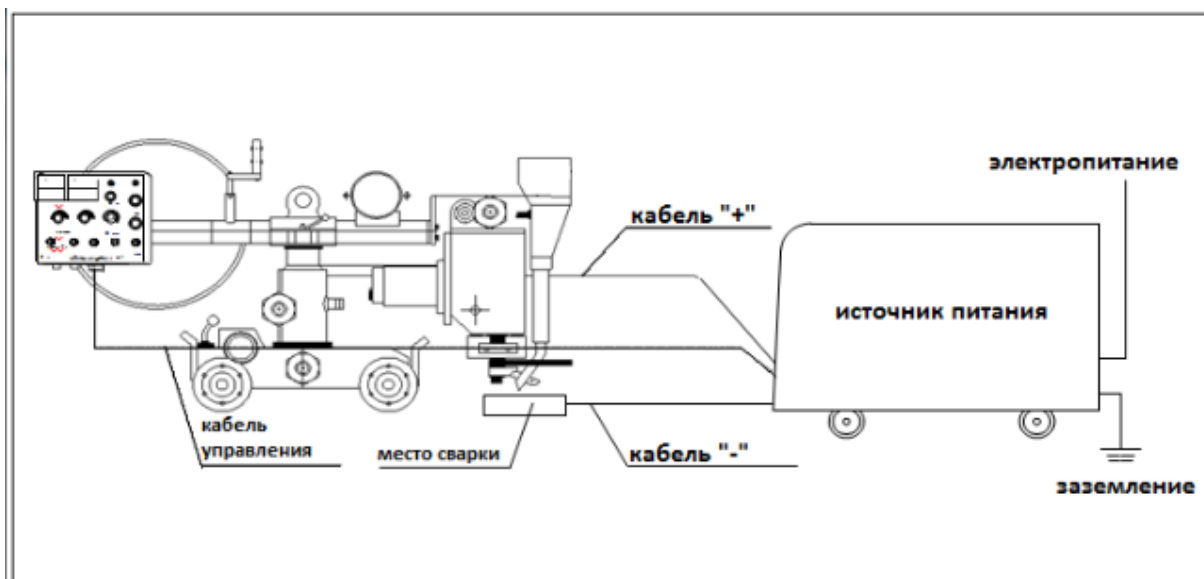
Соединения сварочной системы Pandaweld 1250 [6].
